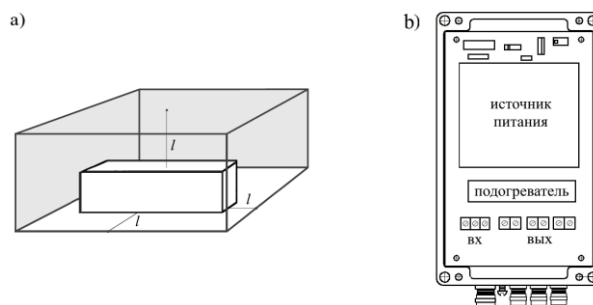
Конструкция ИВЭП малой мощности: а – обеспечение свободного пространства в корпусе, б – расположение элементов в корпусе (вид сверху)
